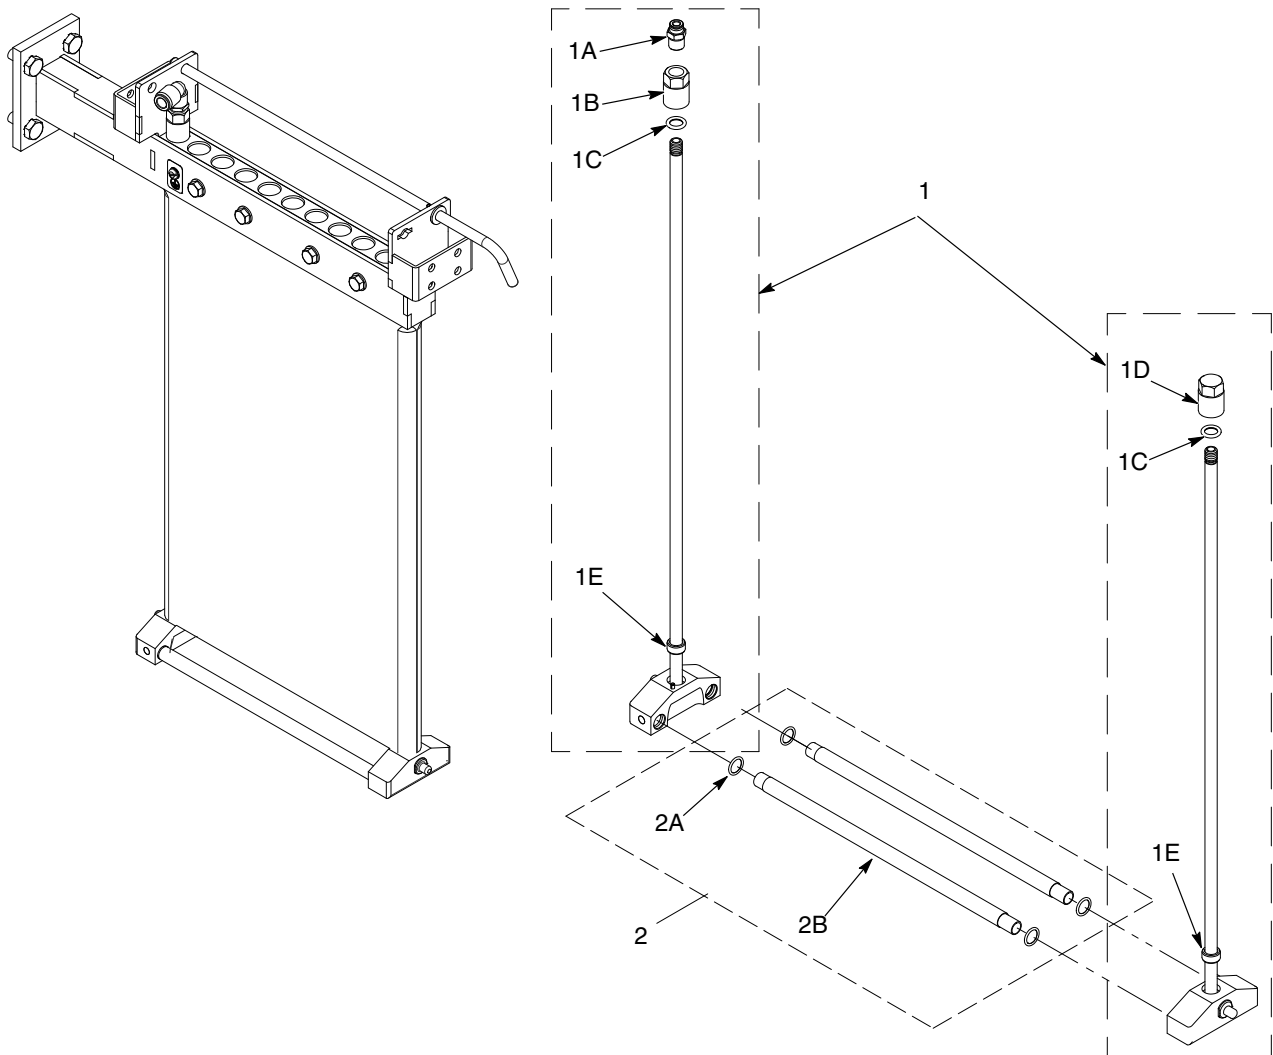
Klemmblockmodul mit Fluidisierung
